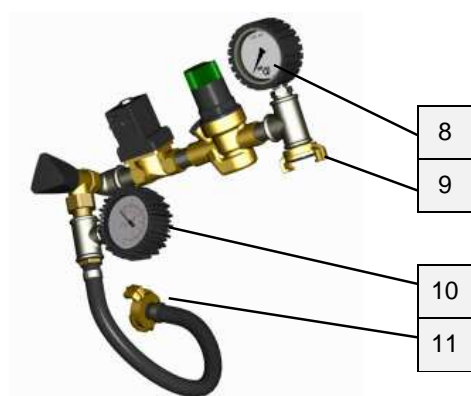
Водопроводная арматура LOTUS XS 00 28 26 13
